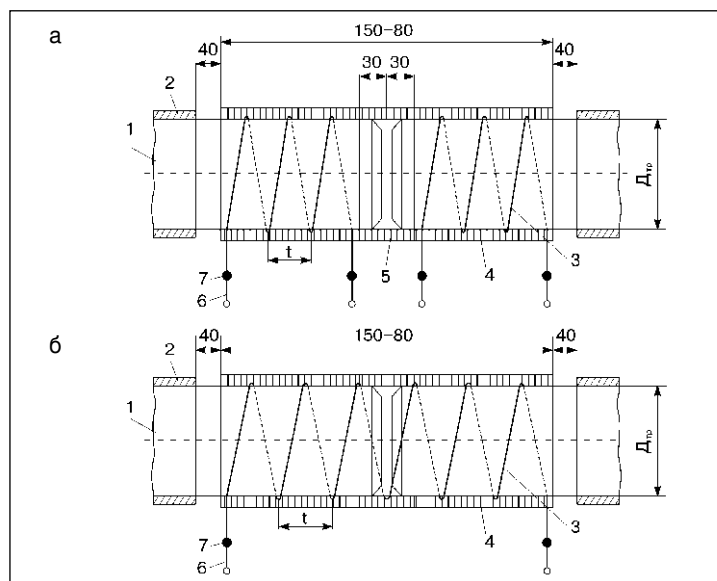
Схемы установки электронагревателей КЭН для подогрева при сварке кромок труб со стационарной антикоррозионной изоляцией: а — при установке КЭН на каждую трубу; б — при установке одного КЭН на свариваемый стык (1 — труба; 2 — стационарная антикоррозионная изоляция; 3 — секции КЭН; 4 — теплоизоляция на КЭН; 5 — теплоизоляция на подогреваемых кромках труб; 6 — токоподводящий кабель; 7 — контактное соединение)
